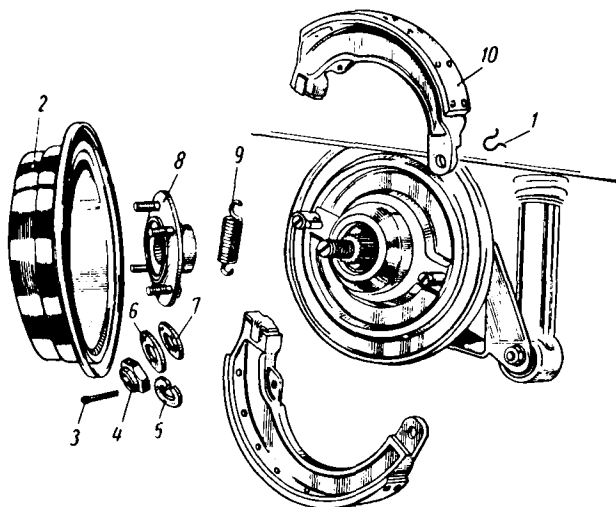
Ступица и тормоз заднего колеса мотороллера ВП-150:
